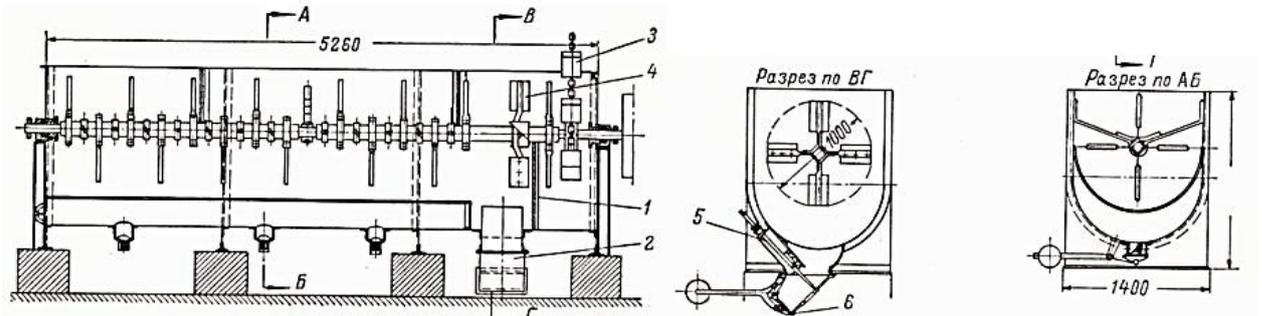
Схема кулачкової коренебульбомийки з металеву односекційною ванною та камневловлювачем: 1 – перегородка; 2 – камневловлювач; 3 – ковшовий транспортер; 4 – черпаки для вивантаження; 5 – засувка; 6 – люк для вивантаження каміння.
